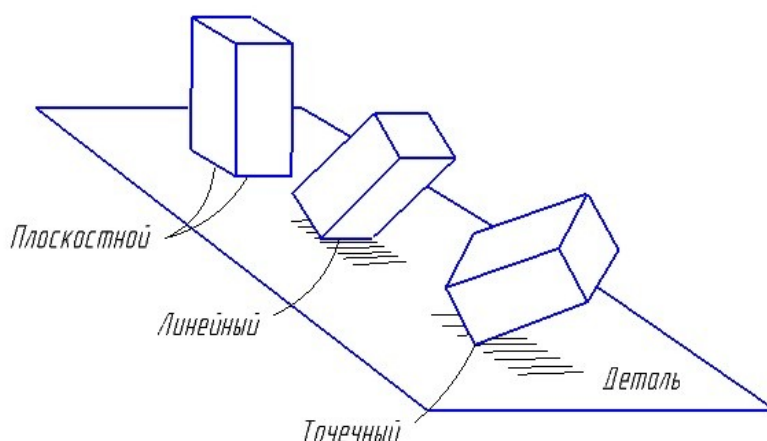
Виды контакта абразивного зерна с обрабатываемой деталью
